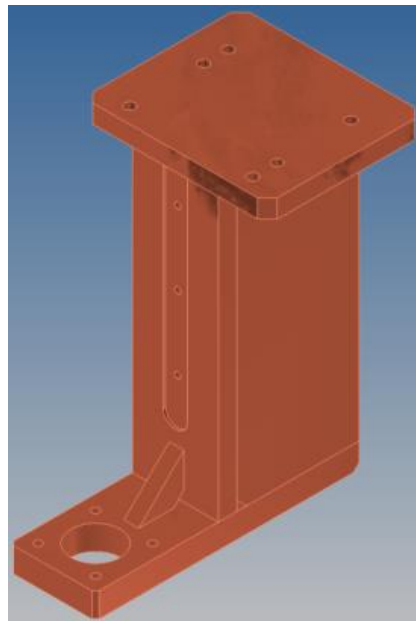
Perfil y alzado de las piezas de la parte superior.
